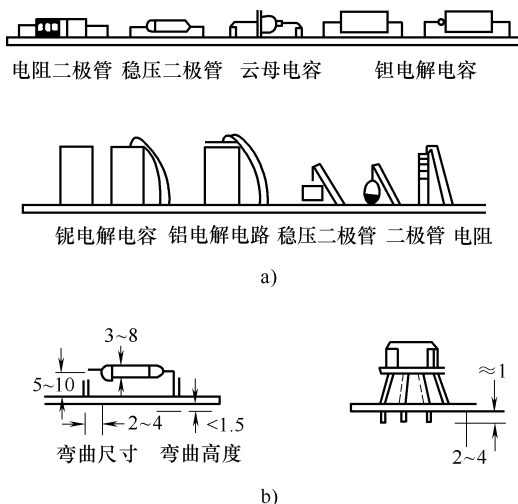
卧式安装和立式安装示意图 (单位: mm)
